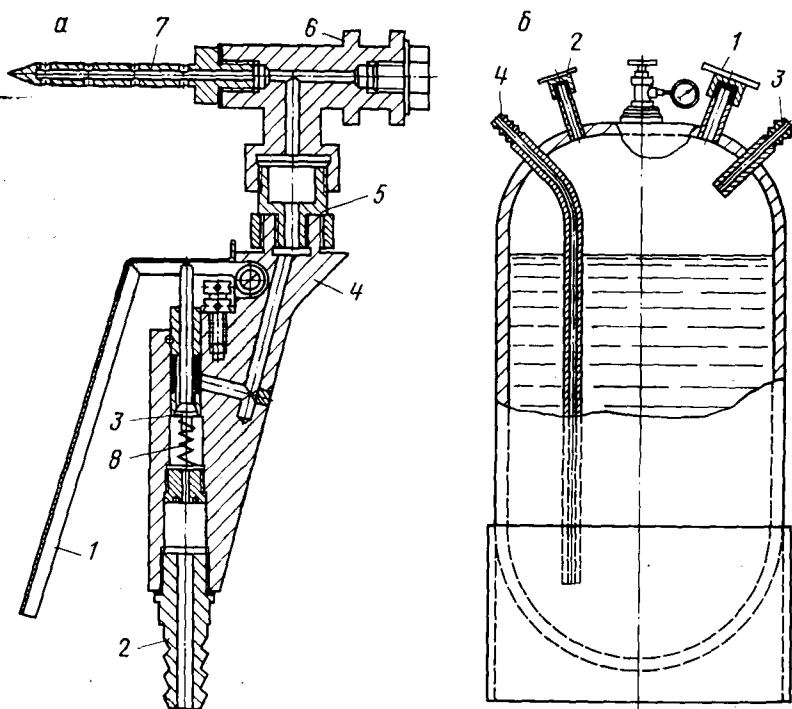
Приспособление для пропитки древесины инъекционным способом: а — пистолет для инъекций: 1 — ручка; 2 — штуцер; 3 — клапан; 4 — корпус; 5 — переходный штуцер; 6 — наконечник; 7 — сменная игла; 8 — пружина; б — баллон для пропиточной жидкости; штуцера для: 1 — заливки антисептика; 2 — спуска воздуха; 3 — подачи сжатого воздуха; 4 — подачи антисептика в пистолет
